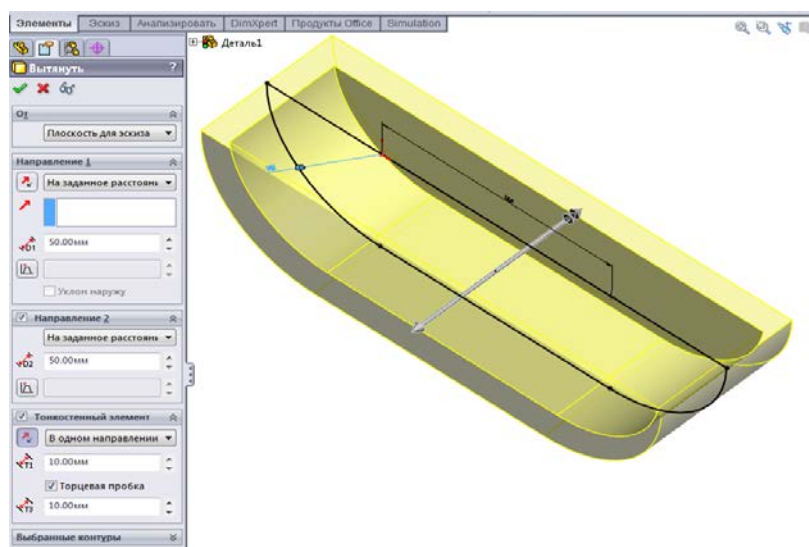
заготовка корпуса двухступенчатого цилиндрического редуктора
